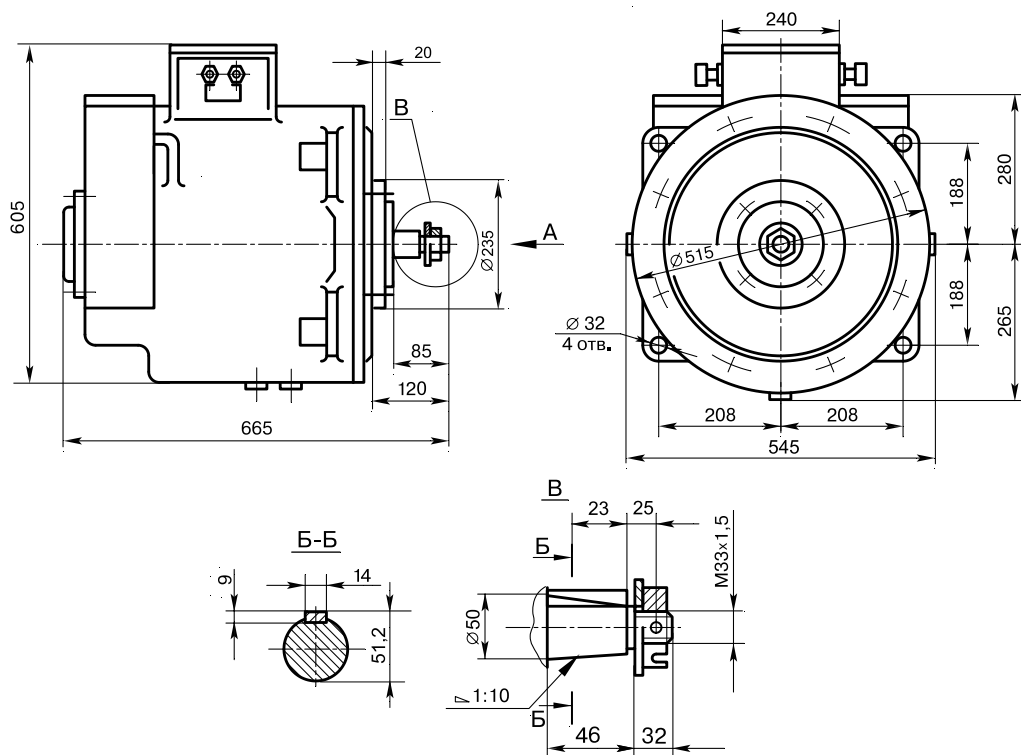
Габаритные и установочные размеры электродвигателя ДРТ-23,5
